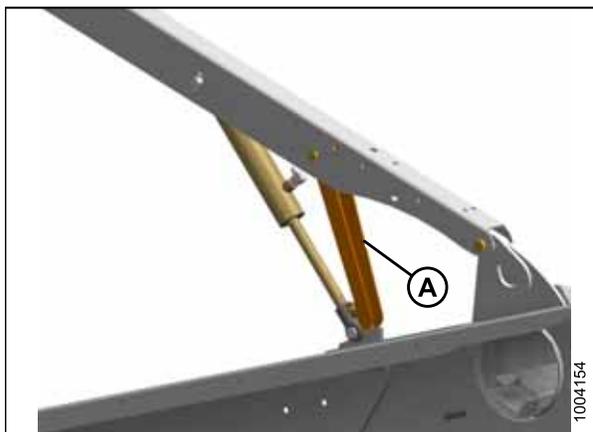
Предохранительный упор подбирающего мотовила — левая сторона
